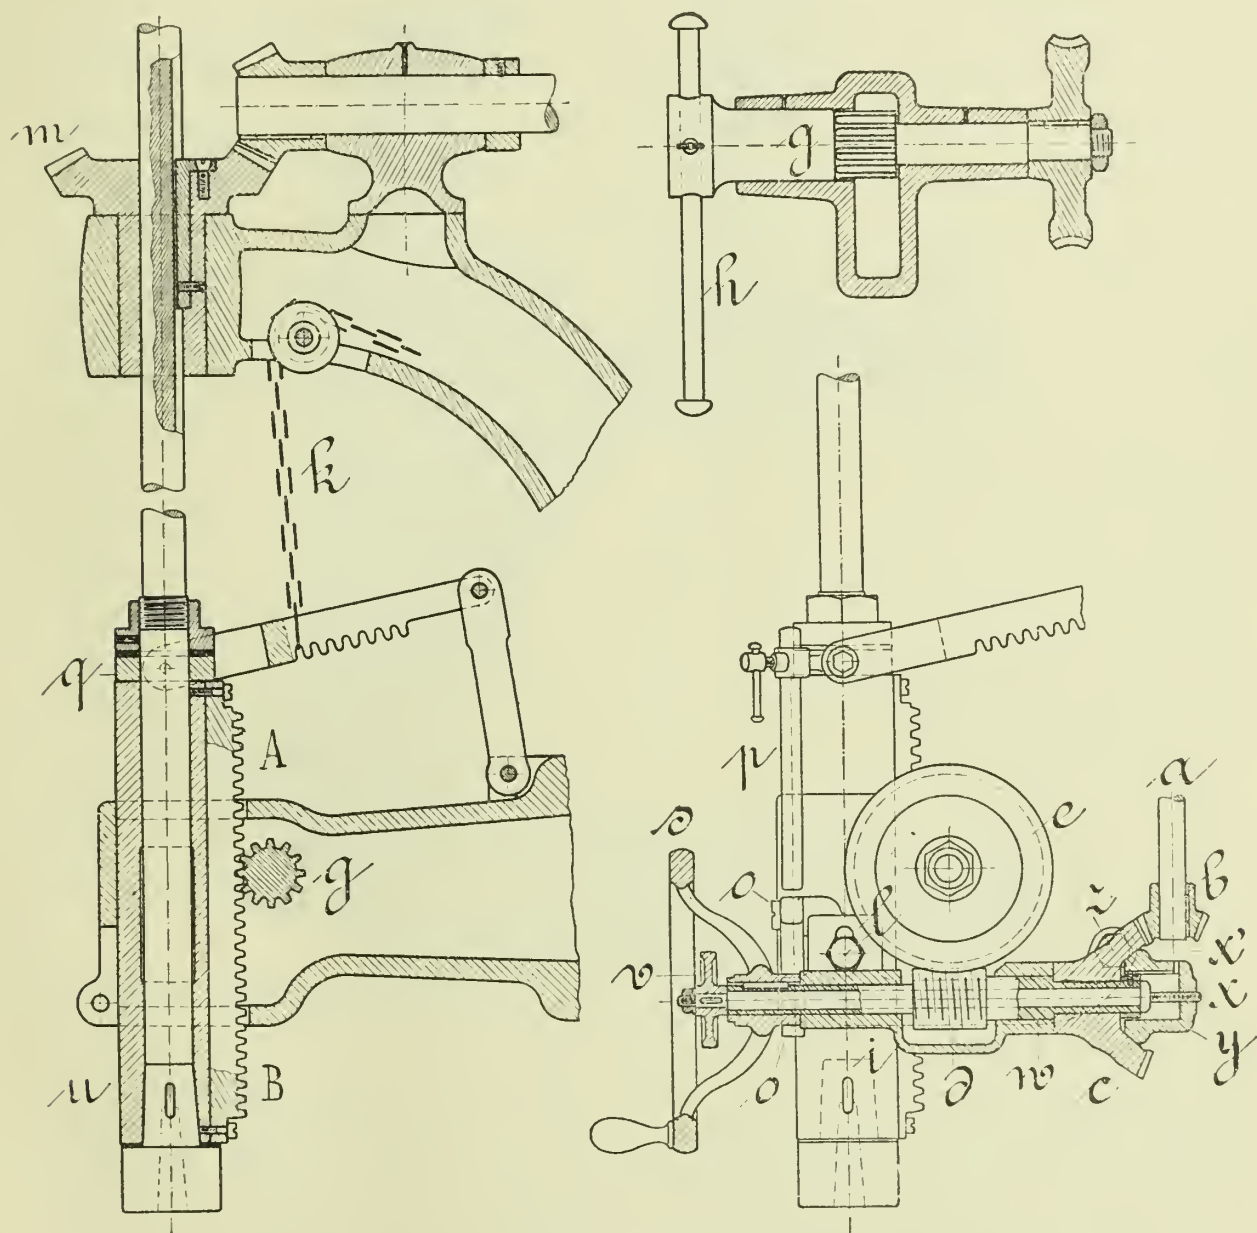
381. Bohrspindel einer amerikanischen Bohrmaschine.
